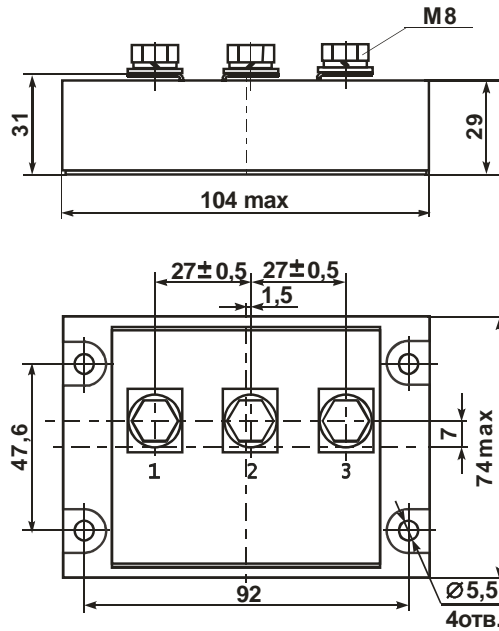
Габаритный чертёж корпуса ДМ
